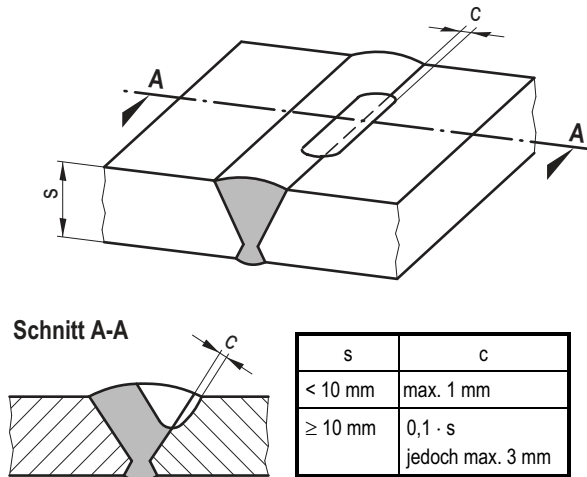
Änderung der Schweißnaht-Ist-Geometrie
